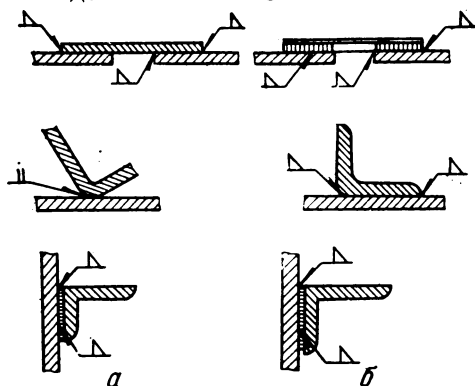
Примеры сварных швов с неполным (а) и полным (б) проплавлением.
